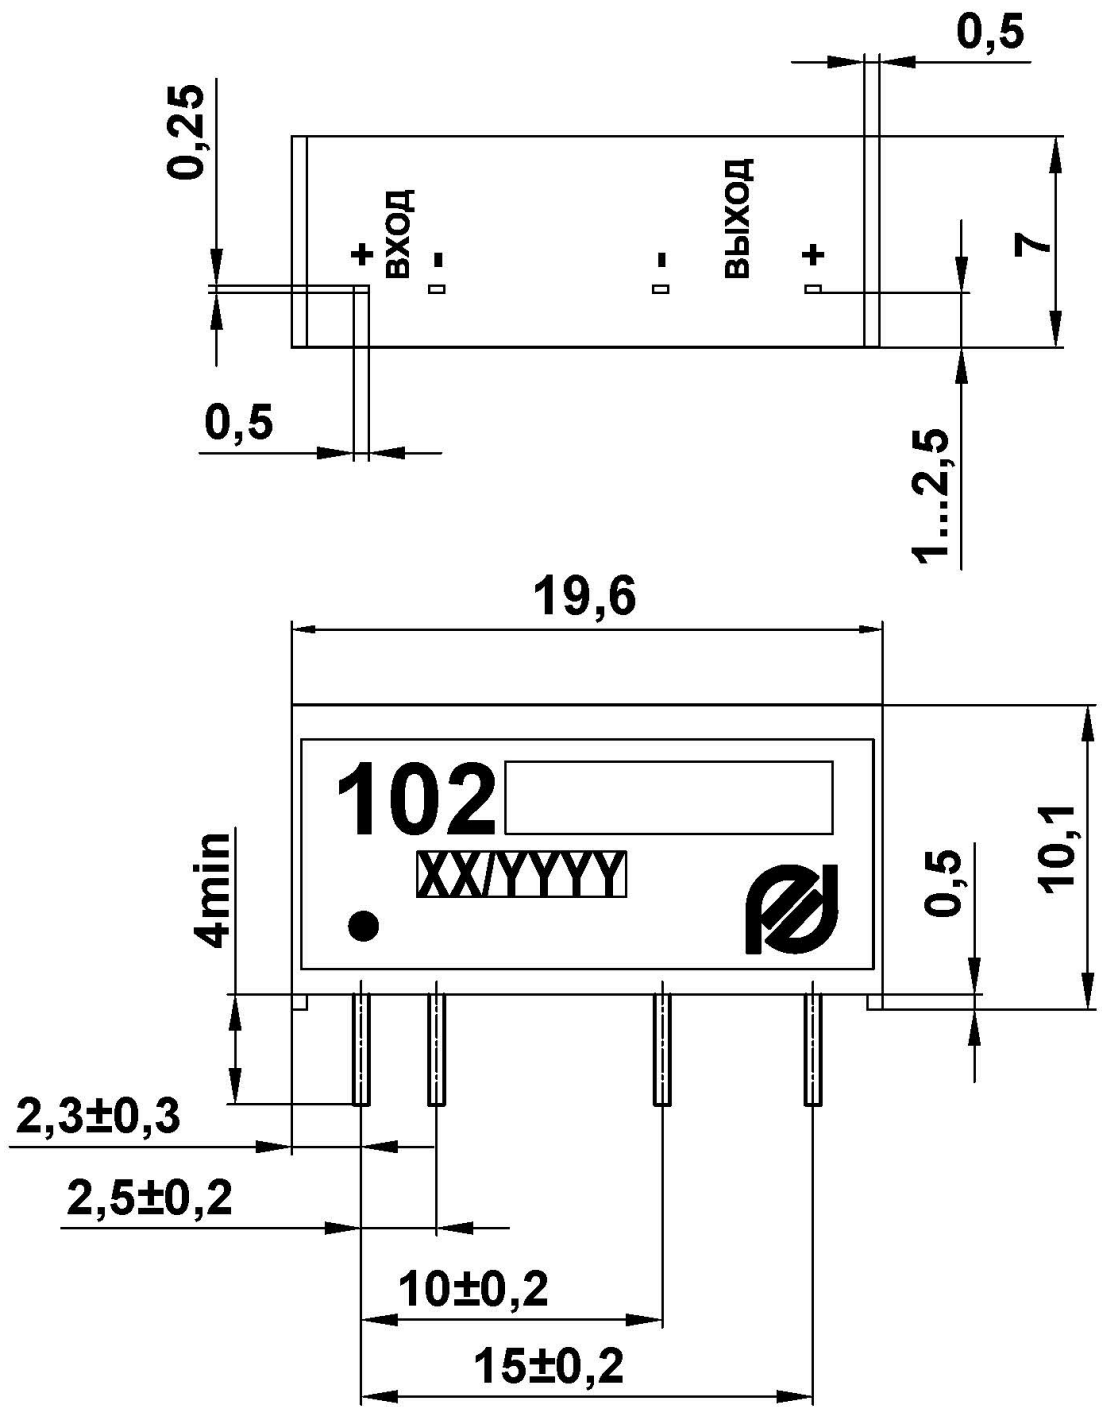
Габаритный чертеж одно- (двух) ваттных одноканальных модулей в конструктиве «В», корпусного исполнения
